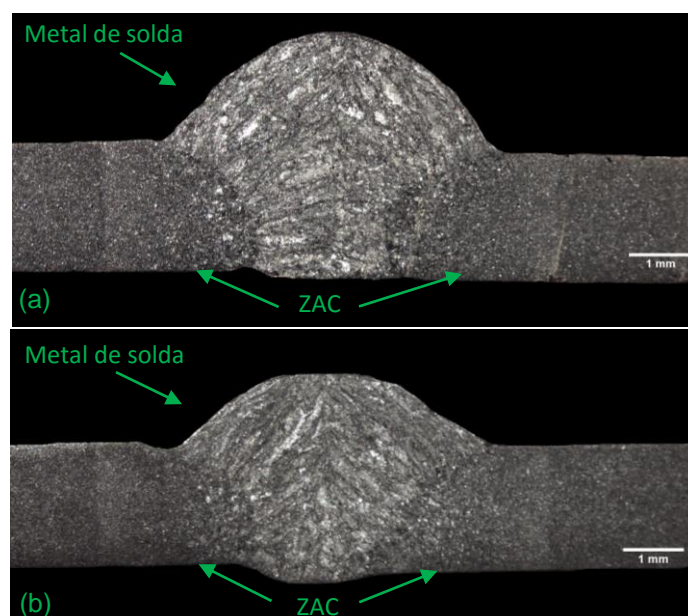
Macrografias indicando as zonas do cordão de solda: (a) baixa energia de soldagem; (b) alta energia de soldagem.
